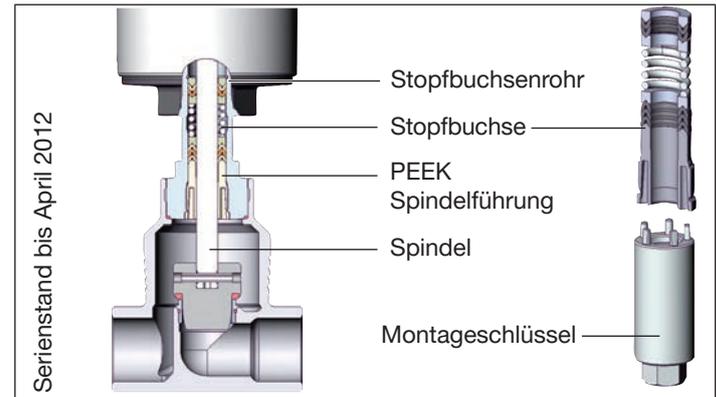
Tausch Stopfbuchse (PEEK-Spindelführung)
